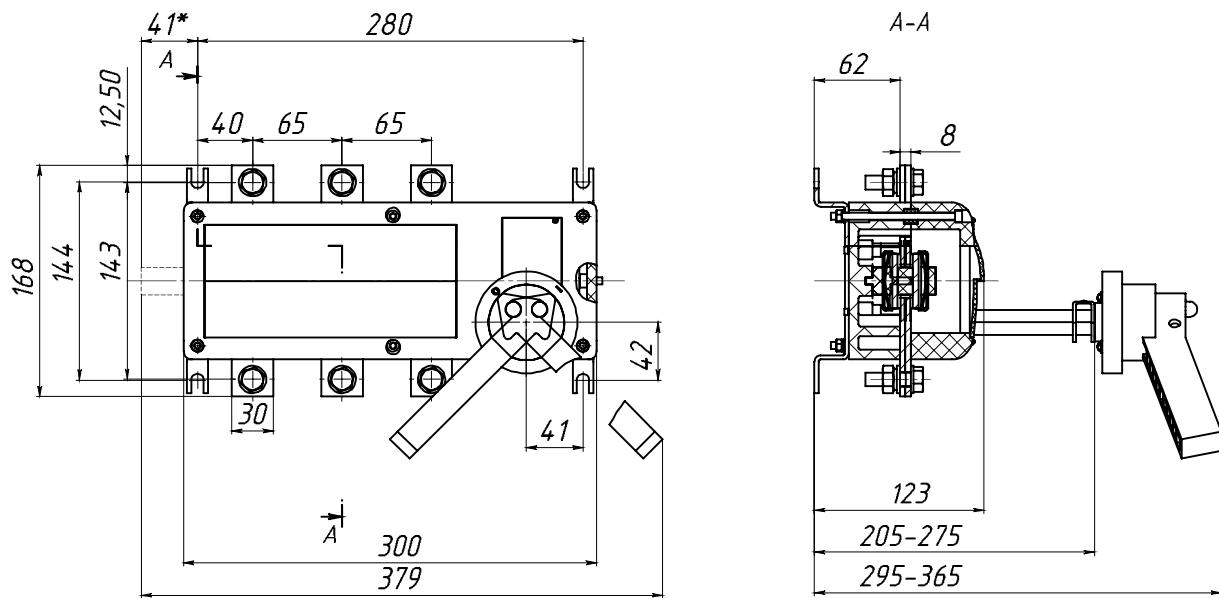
Выключатель-разъединитель ВНК-37-31130-32 УХЛЗ
